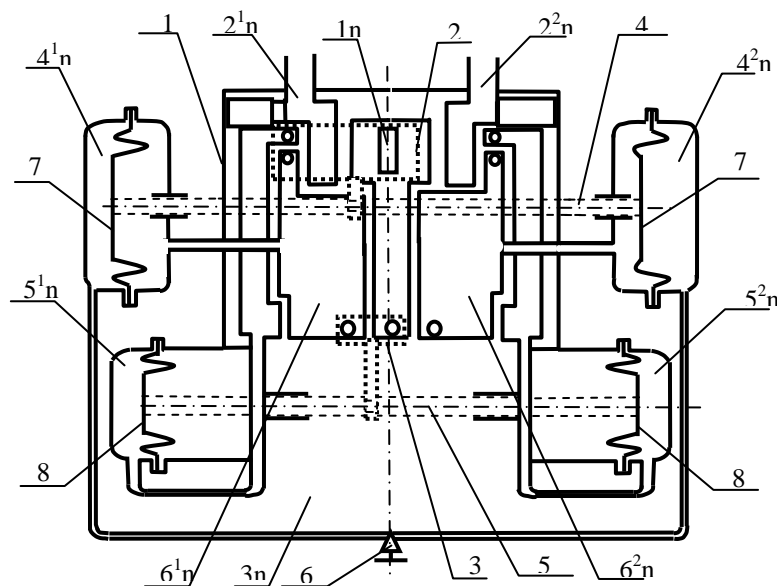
Схема попарного пульсатора: 1 – корпус; 2 – верхній клапан; 3 – нижній клапан; 4 – вісь верхня; 5 – вісь нижня; 6 – регулювальний гвинт; 7 – мембрани верхні; 8 – мембрани нижні.
